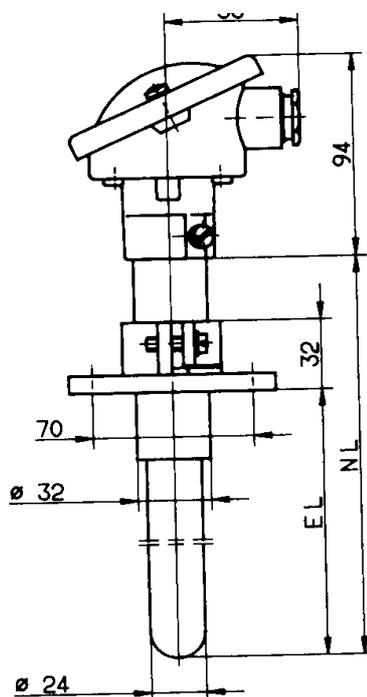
推入式带 A 型端子头 AK 型热偶外形尺寸 3
